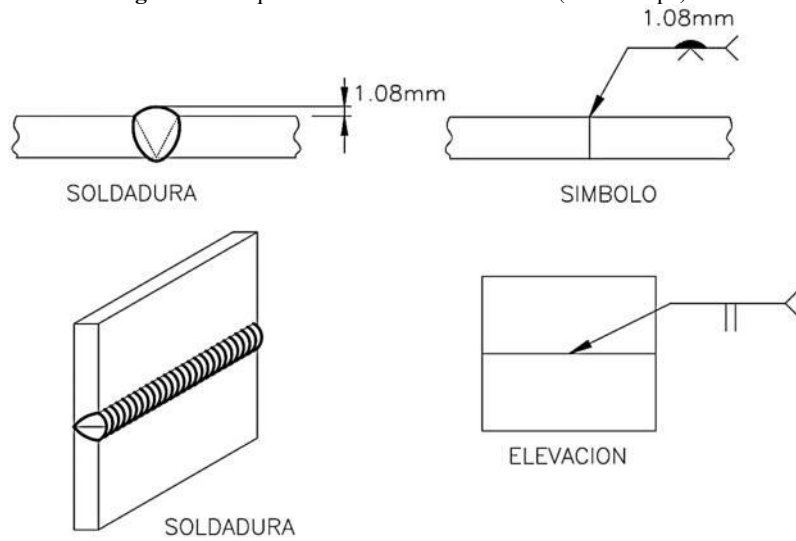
Esquema de soldadura - placa base y columna (Junta en T)
